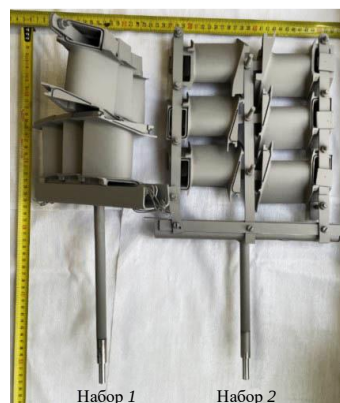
Внешний вид имитаторов крупногабаритных деталей газотурбинного двигателя и образцов-свидетелей после нанесения покрытия
